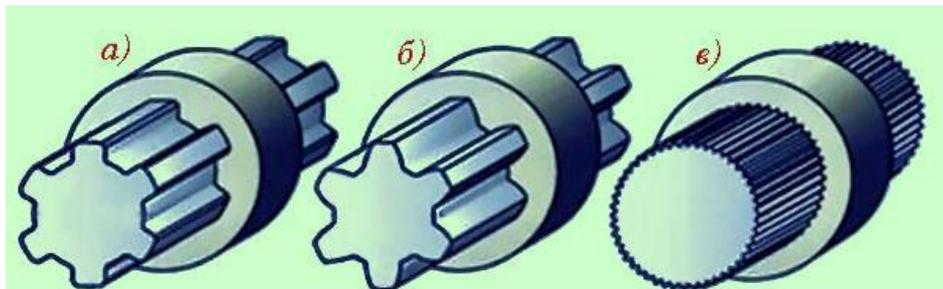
Форма выступов зубьев шлицевого соединения:
